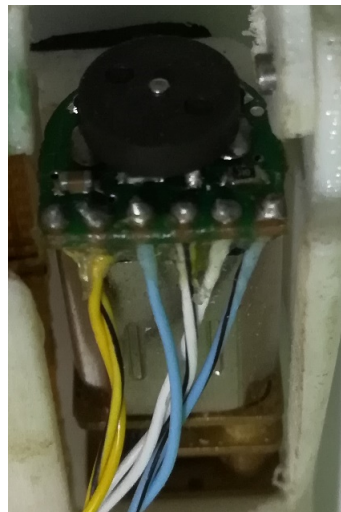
Encoder magnético soldado al motorreductor.
